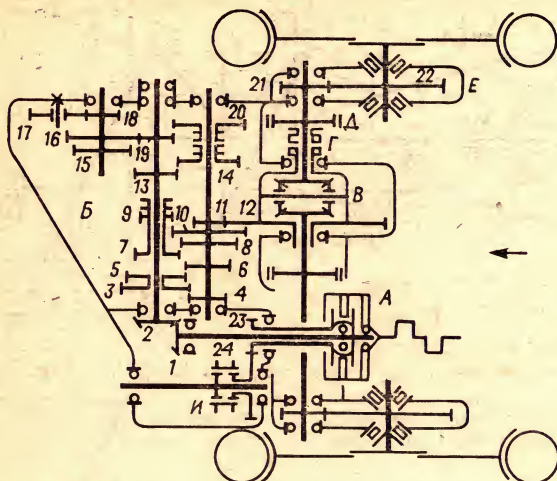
Кинематическая схема силовой передачи самоходного шасси Т-16М:
